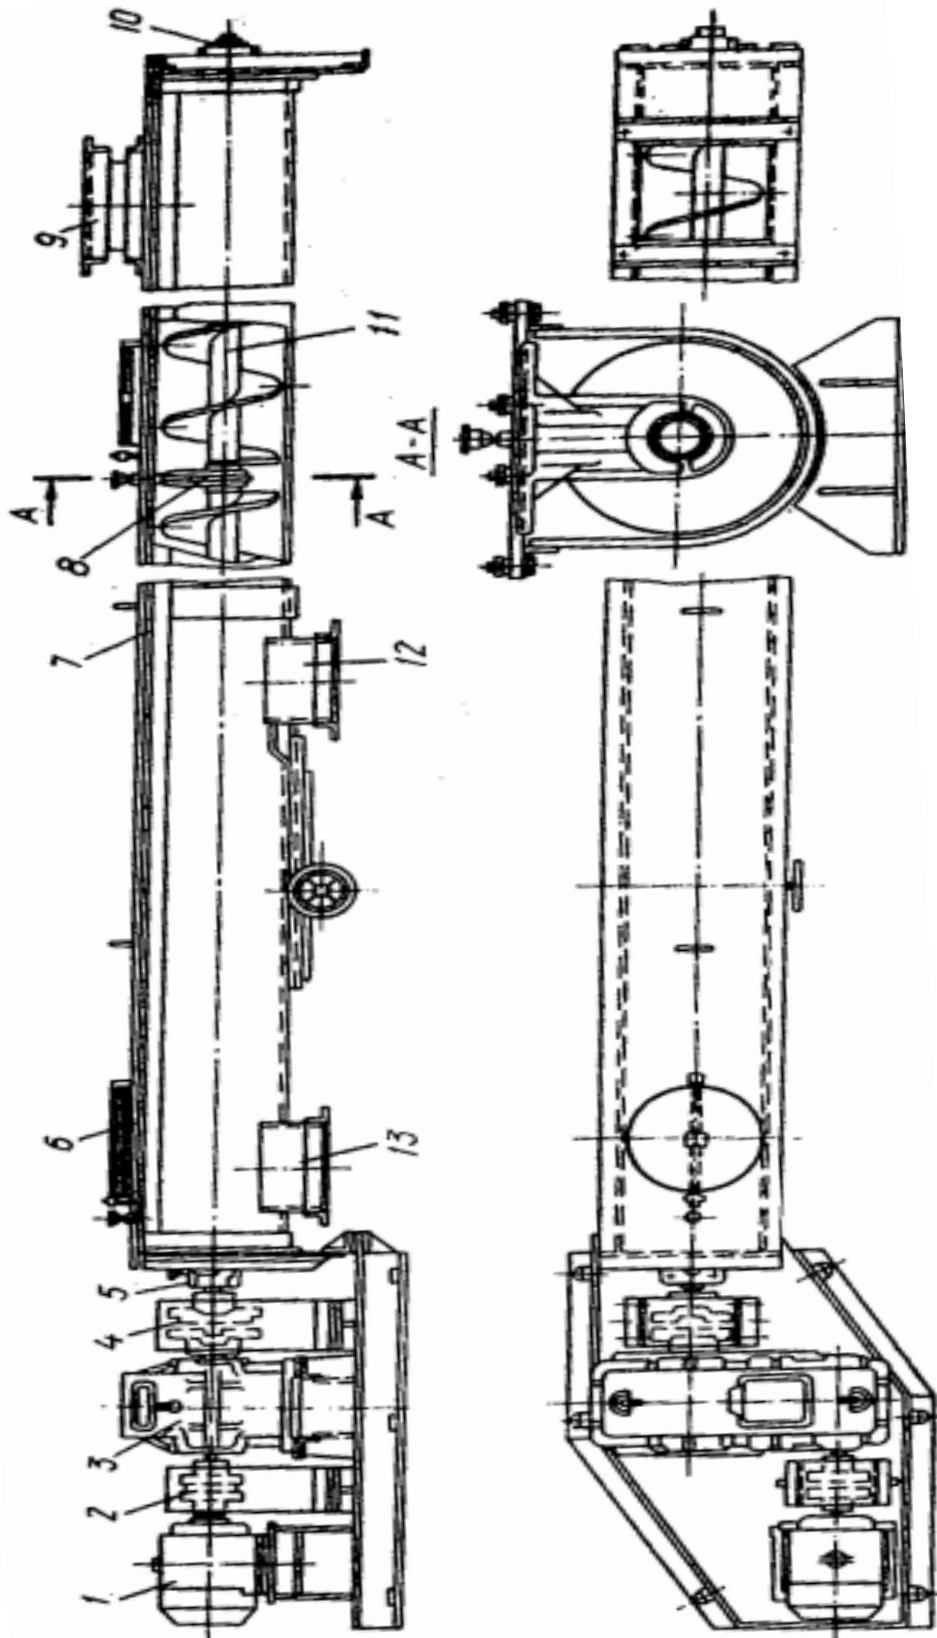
Схема гвинтового конвеєра: 1 — двигун; 2 і 4 — муфти; 3 — редуктор; 5, 8, і 10 — підшипникові вузли; 6 — оглядовий люк; 7 — жолоб; 9 — завантажувальний патрубок; 11 — вал з гвинтом; 12 — проміжний завантажувальний патрубок; 13 — розвантажувальний патрубок.
